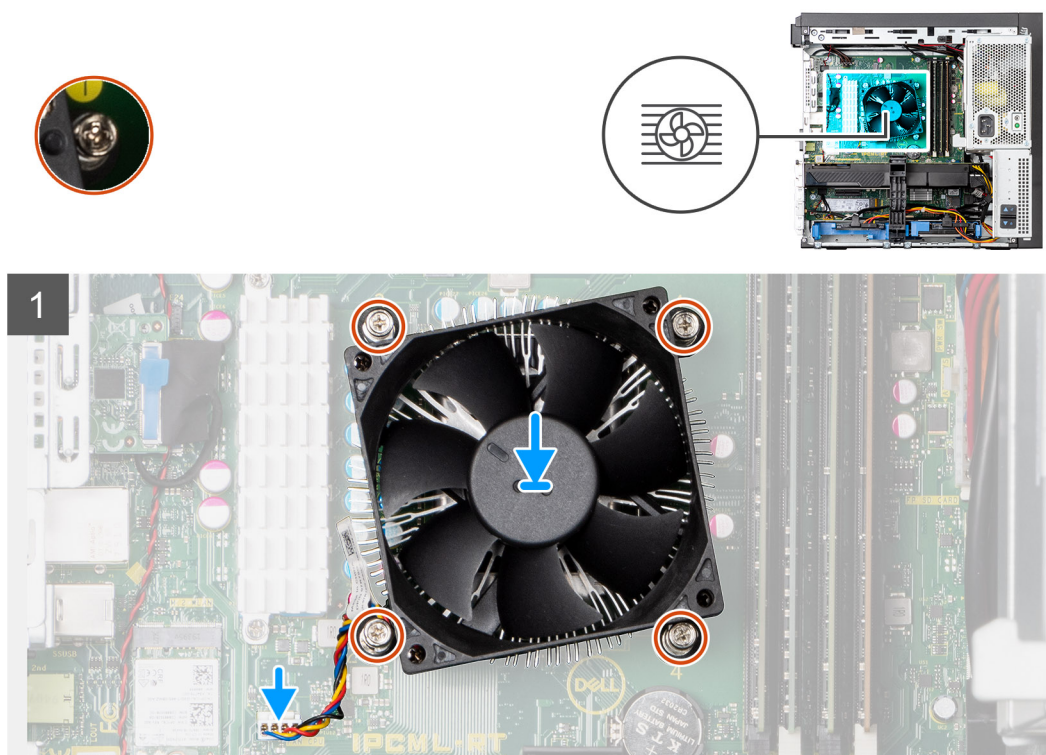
Conjunto do dissipador de calor - CPU de 65 W ou 80 W
